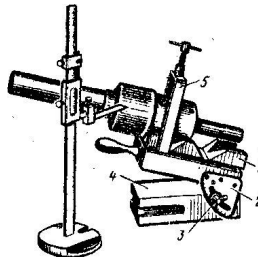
Пристрій з призмою для розмічання деталей під кутом
